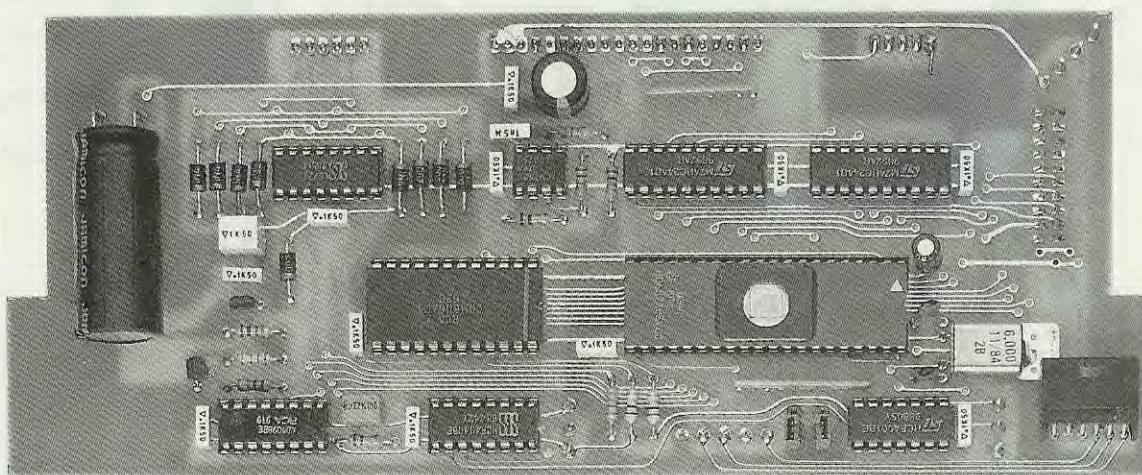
Foto dello stampato LX.994 con tutti i componenti già montati.
